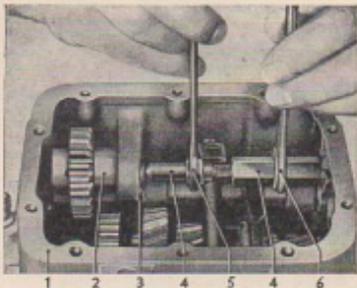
Achse für Rücklauf mit Ausrißschraube aus Getriebegehäuse herausschieben
